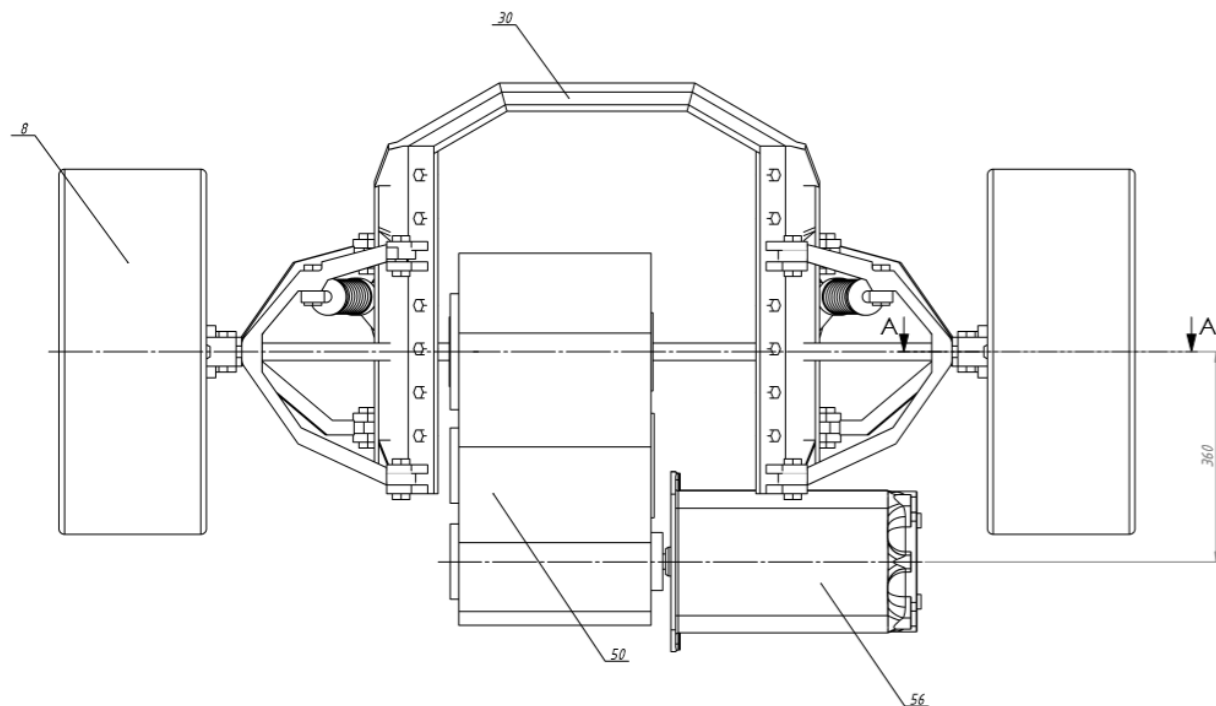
Загальний вигляд переднього приводу(Вид знизу).
